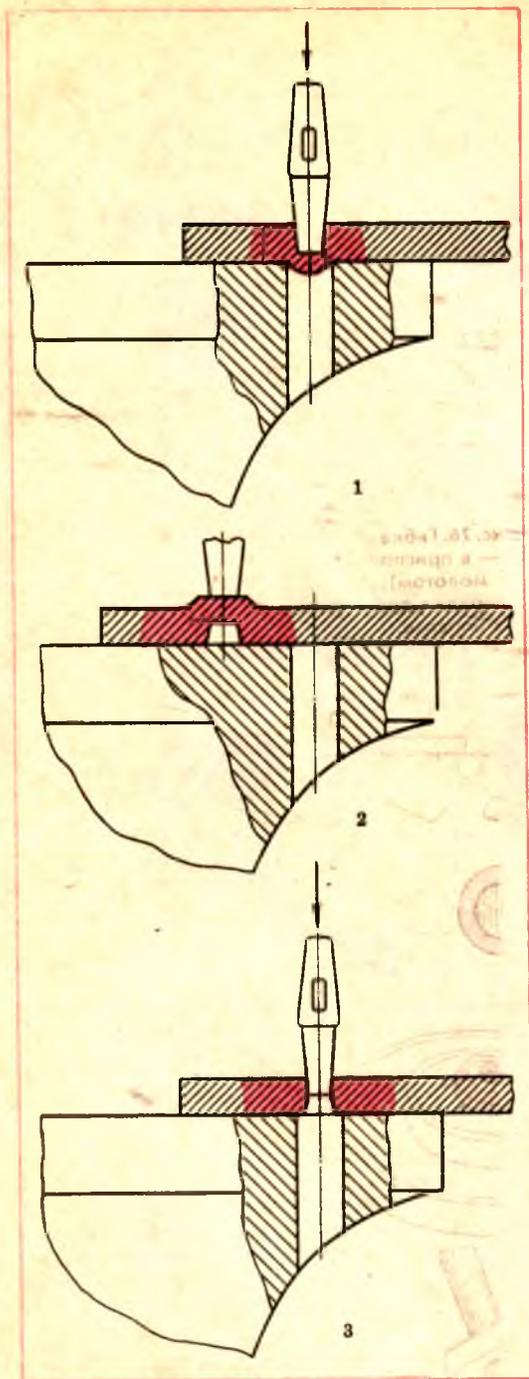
Пробивка отверстий: 1 — предварительная пробивка; 2 — переворот заготовки; 3 — окончательная пробивка
